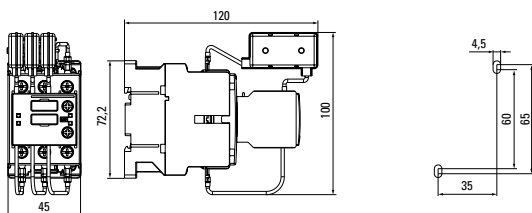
Габаритные и установочные размеры контакторов КМЭК 20
